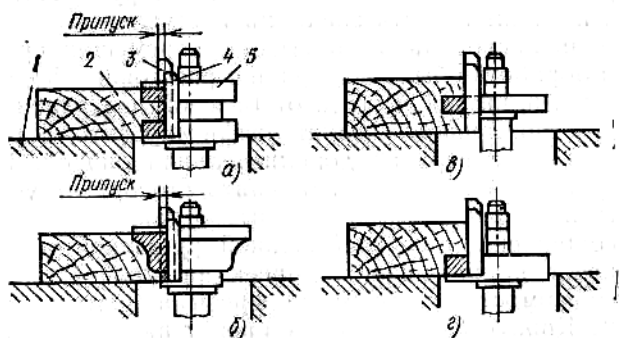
Схема обработки на фрезерном станке: а — гребня, б — плинтуса, в — шпунта, г — фальца; 1 — стол, 2 — деталь, 3 — задняя линейка, 4 — передняя линейка, 5 — фреза
